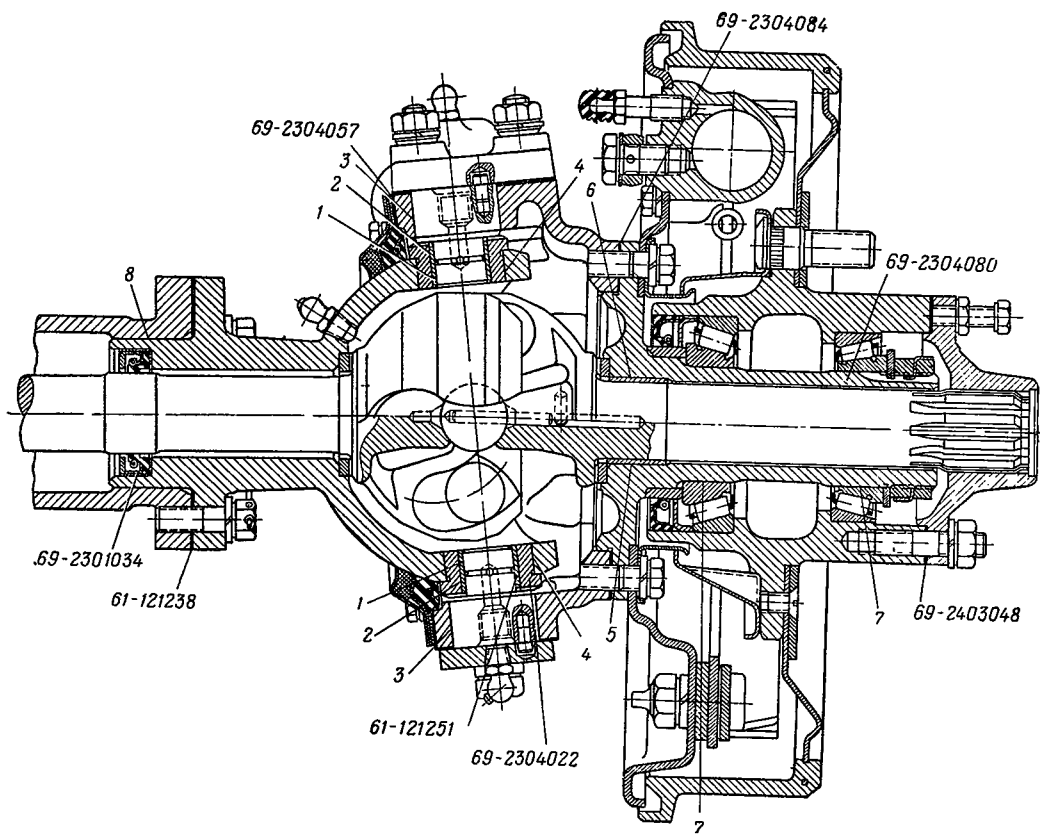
Места сопряжений при сборке поворотного кулака и установке ступицы с тормозным барабаном
